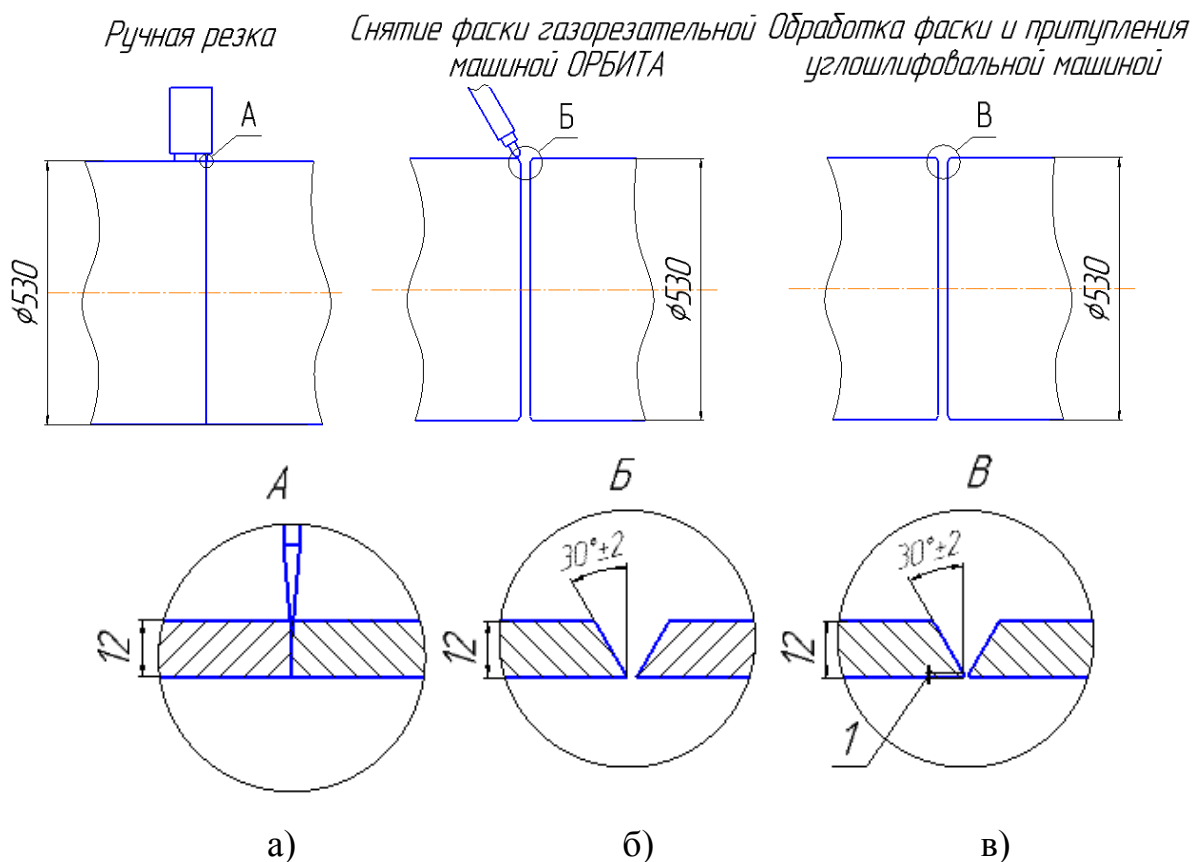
Старая технология подготовки стыков к сварке
